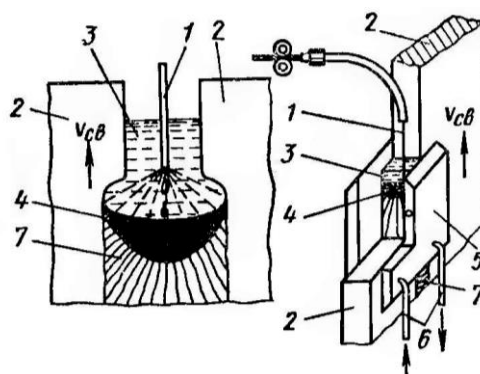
Схема процесса электрошлаковой сварки
